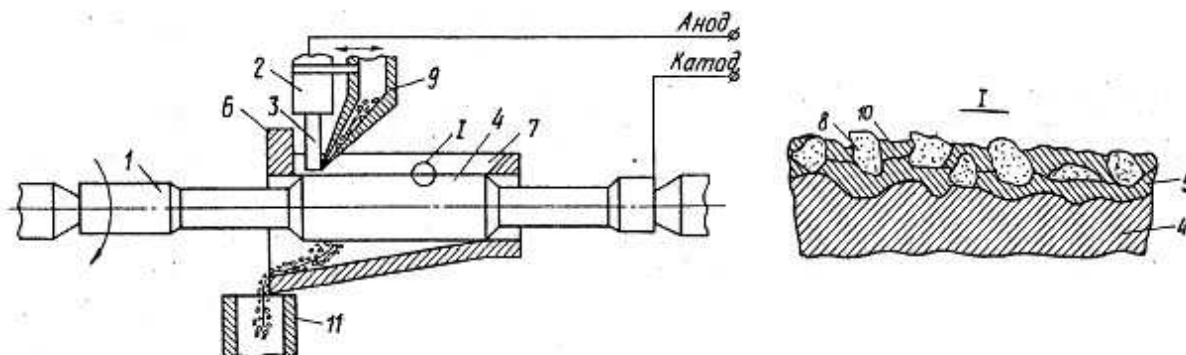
Технологическая оснастка для изготовления притиров для доводки глубоких прецизионных отверстий: 1 – корпус притира; 2 – искровое устройство; 3 – электрод; 4 – рабочая поверхность притира; 5 – слой меди (первичный); 6 – обечайка; 7 – прорезь; 8 – абразивные частицы; 9 – подающее устройство; 10 – слой меди (вторичный); 11 – накопитель
